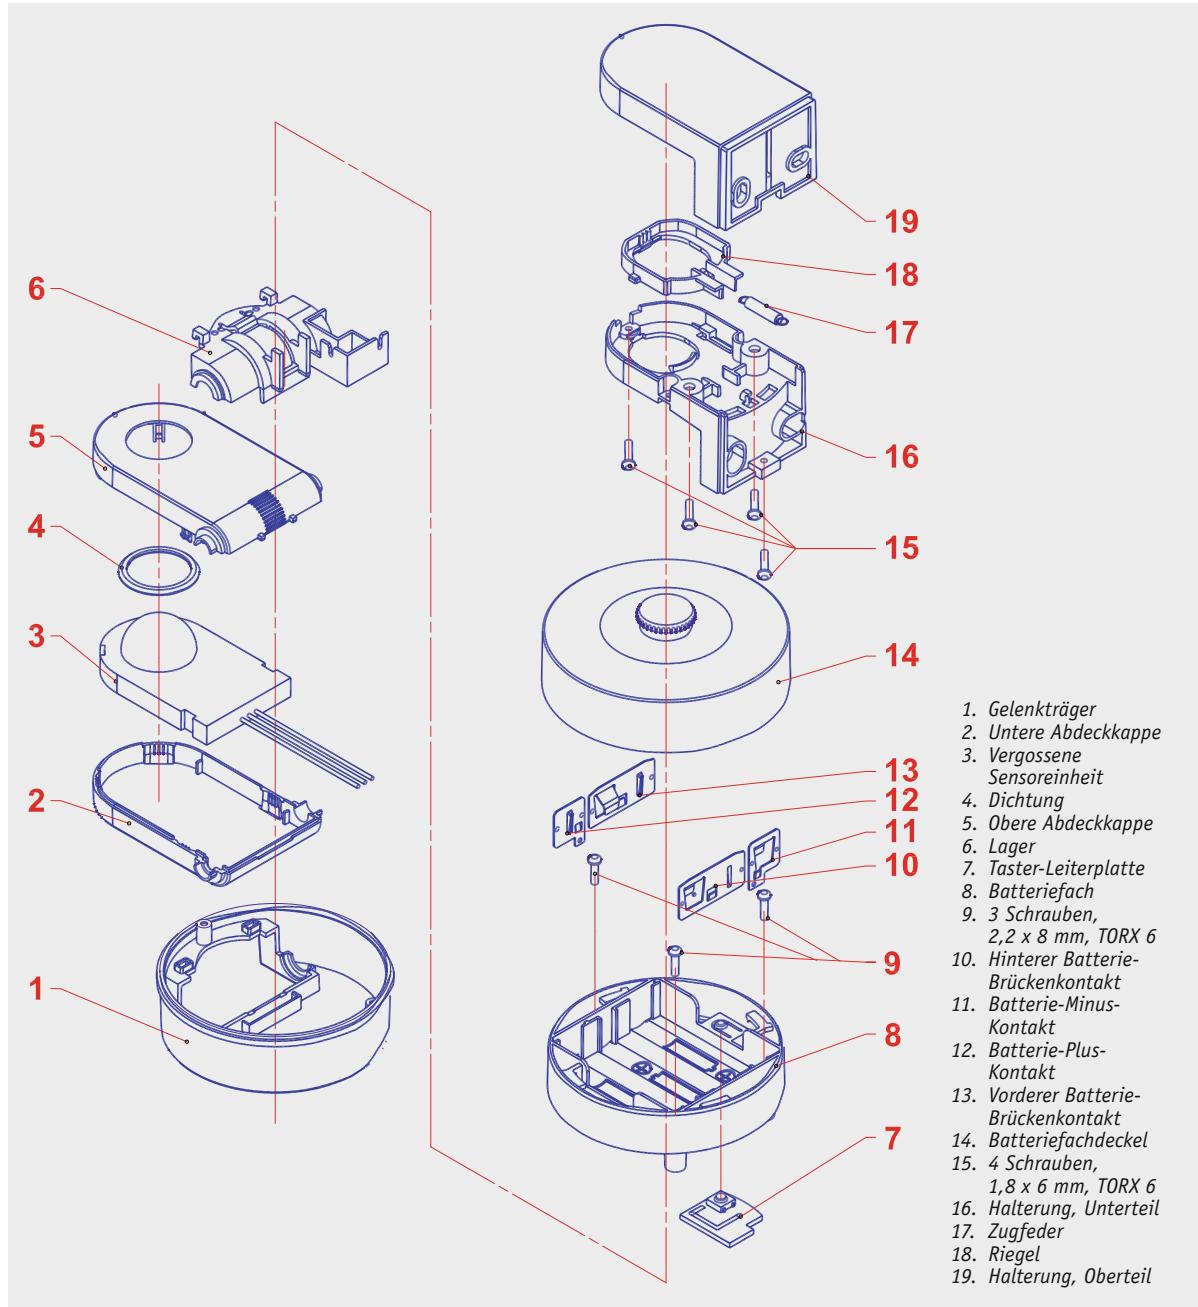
Die Explosionszeichnung gibt einen Überblick über den mechanischen Aufbau.
